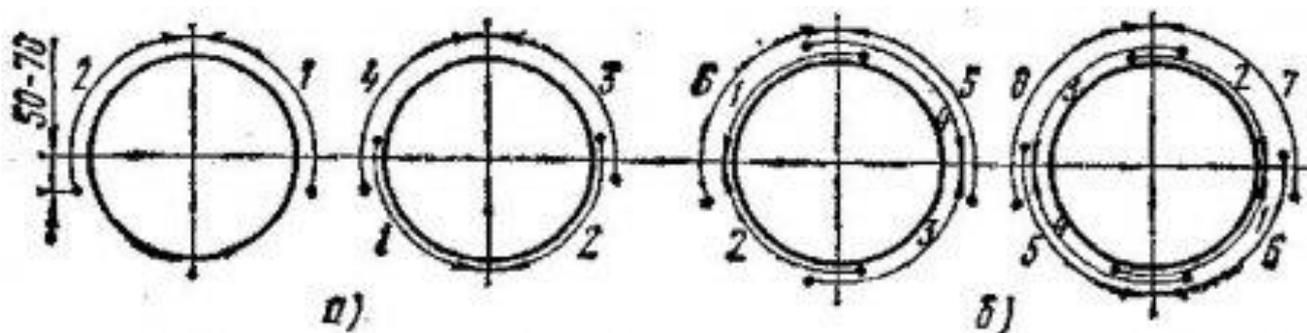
Схема сварки стыка трубы: а - первого слоя, б - второго слоя
